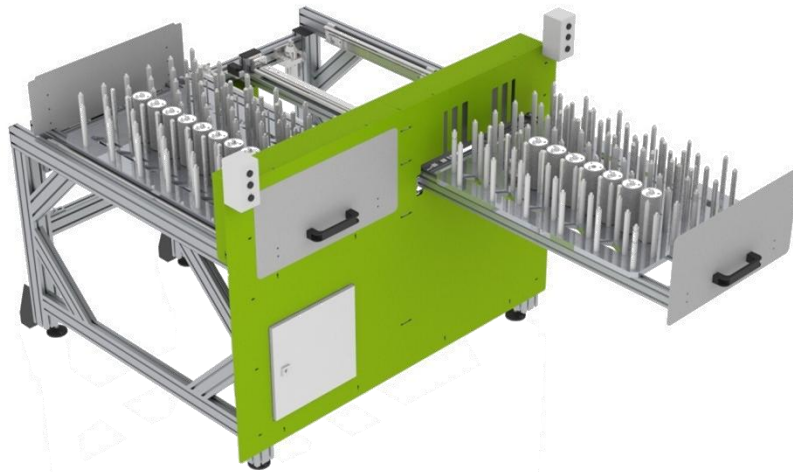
Jednoduchý manuální posuvný stůl [5]
